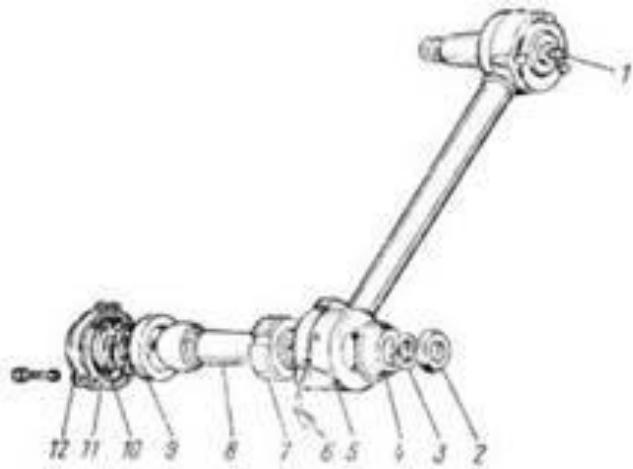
Реактивная штанга: 1 - масленка; 2 - гайка; 3 -шайба пружинная; 4 - сальник; 5 - штанга; 6 - заклепка; 7 - вкладыш внутренний; 8 - палец; 9 - вкладыш наружный; 10 - пружина; 11 - прокладка; 12 – крышка
